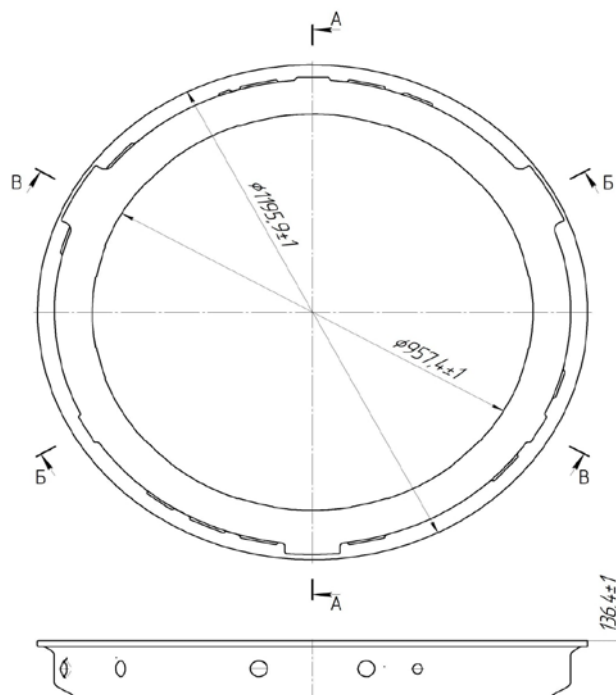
Внешний вид и габаритные размеры отливки детали без литниково-питающей системы
